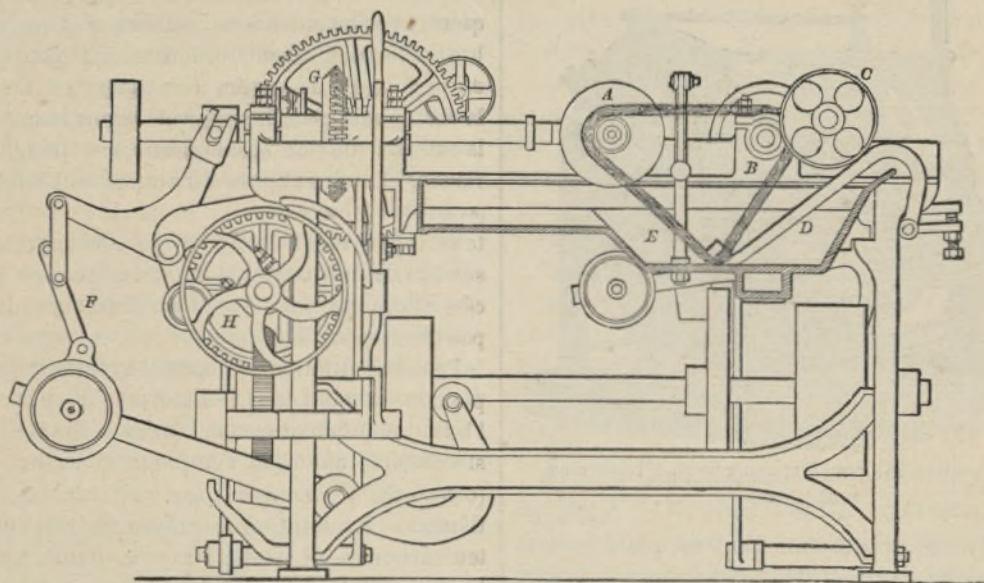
Machine à tremper pour le fil à teindre en rouge ture.
